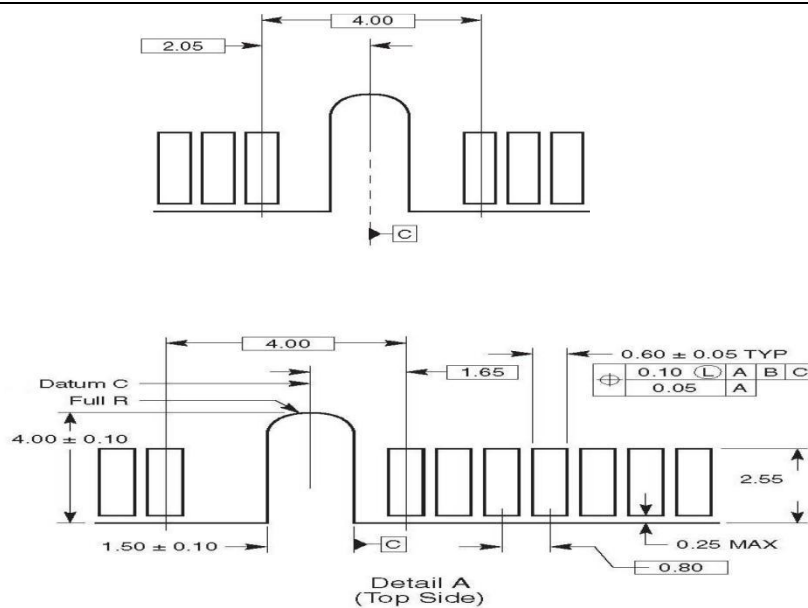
金手指 TOP 和 BOTTOM AB 处细节尺寸
